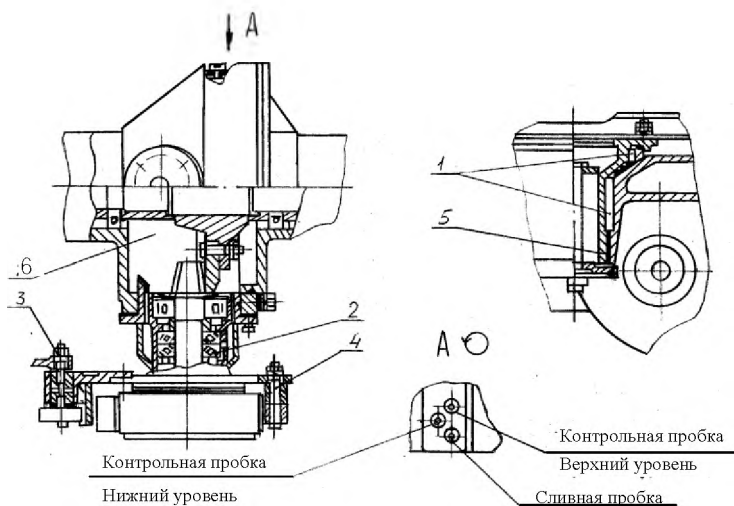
Схема смазки механического оборудования тележки вагона АКСМ-60102: 1 - полости поворотного соединения; 2 - трущиеся поверхности; 3, 4 - вкладыши; 5 - вкладыши; 6 - полость главной передачи
